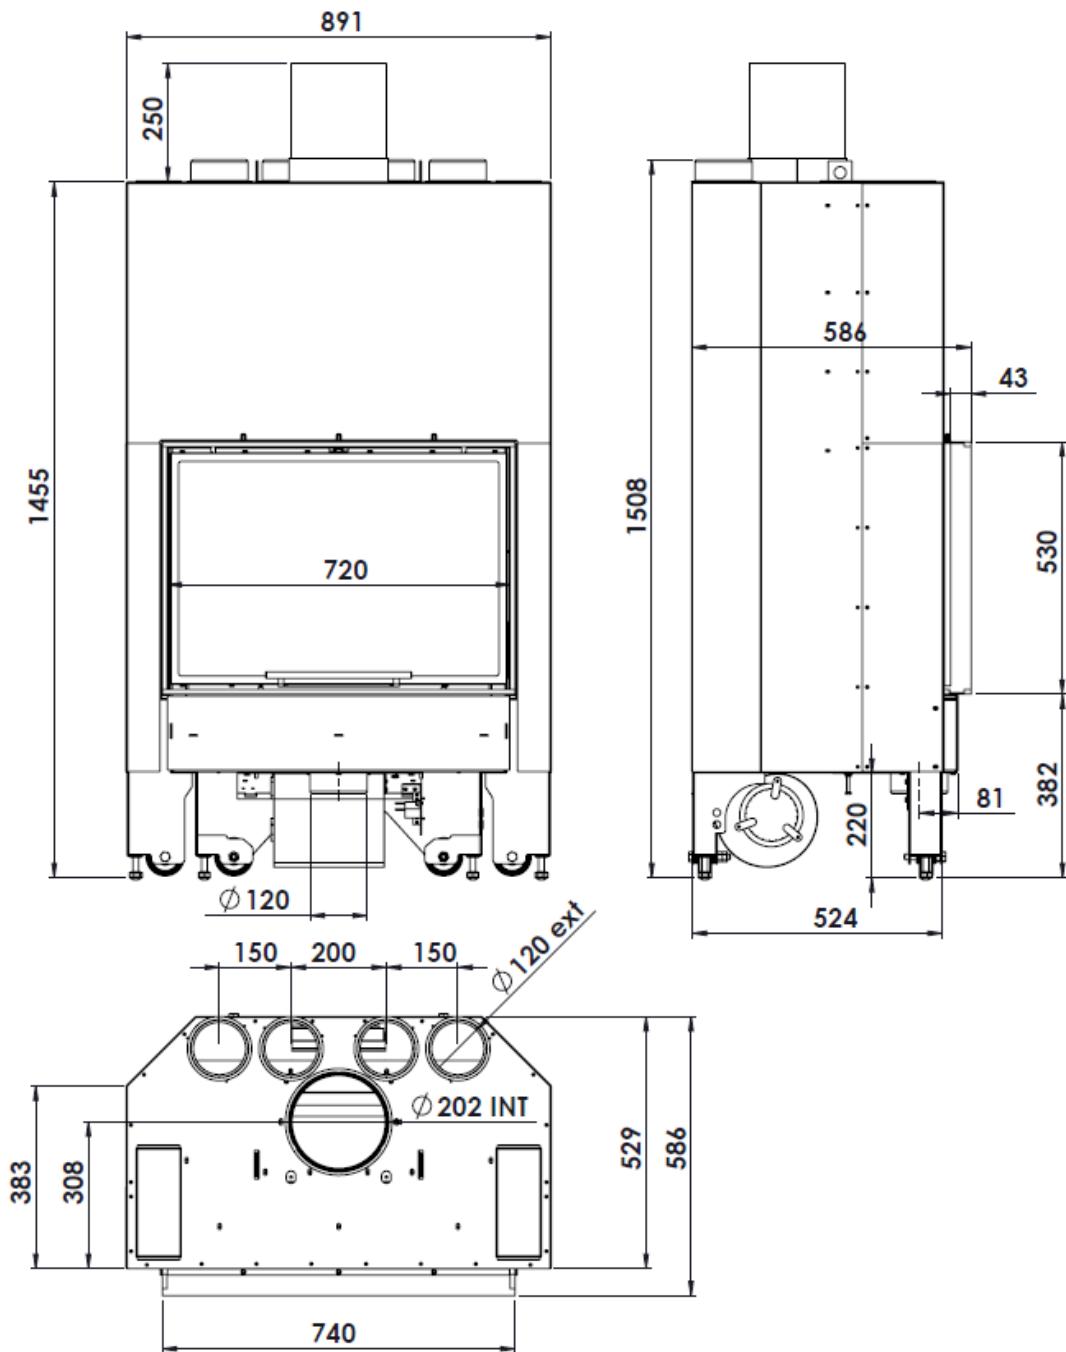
Dimensiones en mm del aparato ITACA 80 eco
